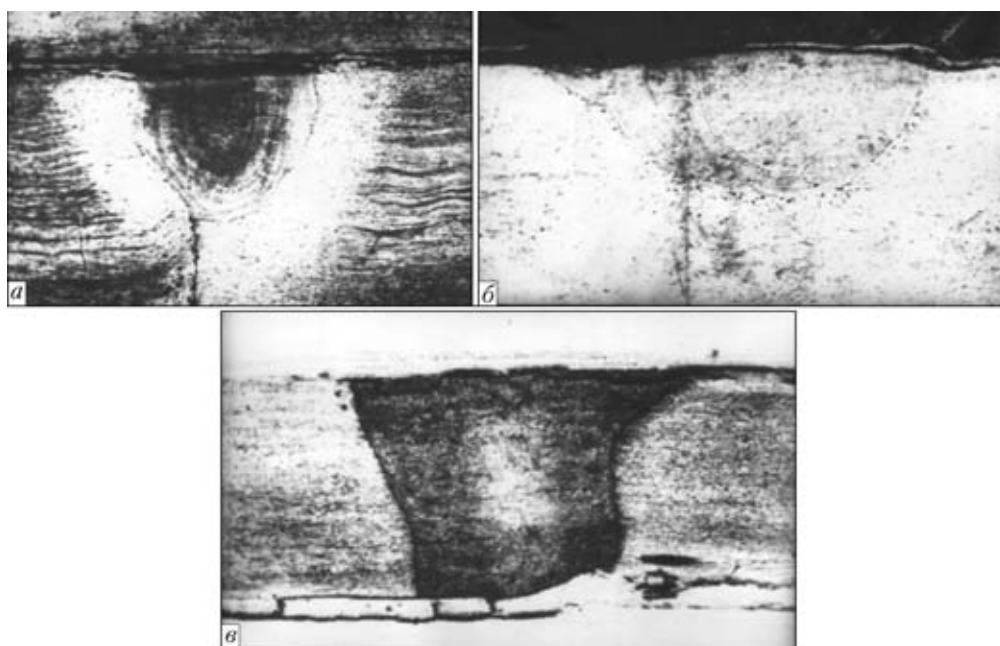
Макроструктура стыковых соединений из стали 08X17T ($\delta = 3,5$ мм): *a* — лазерная сварка; *б* — плазменная сварка; *в* — гибридная сварка
